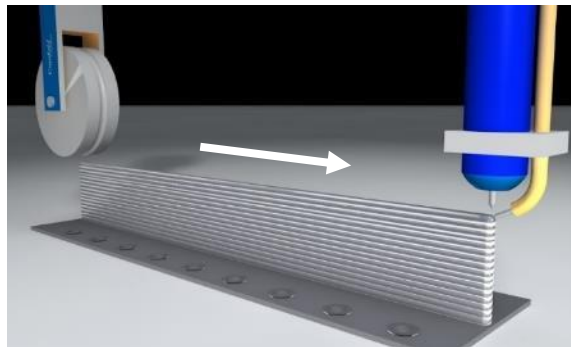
Esquema del equipo de laminado y soldadura mediante WAAM.
